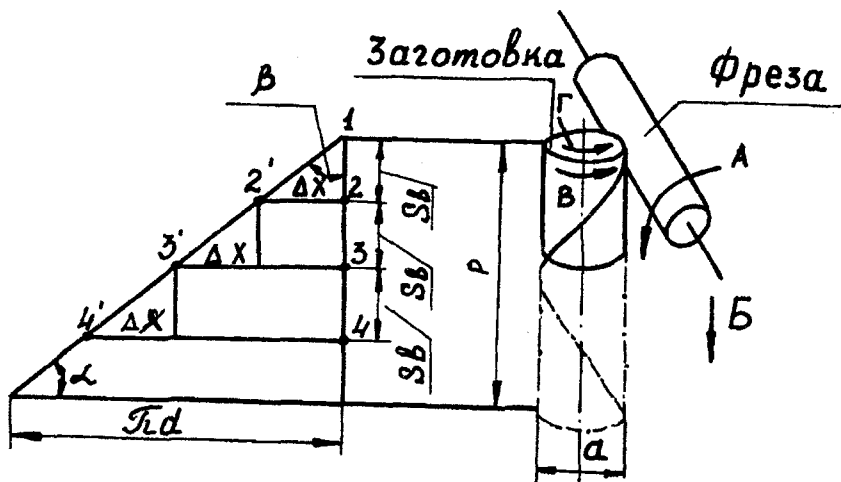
Схема образования зубьев цилиндрического косозубого колеса
